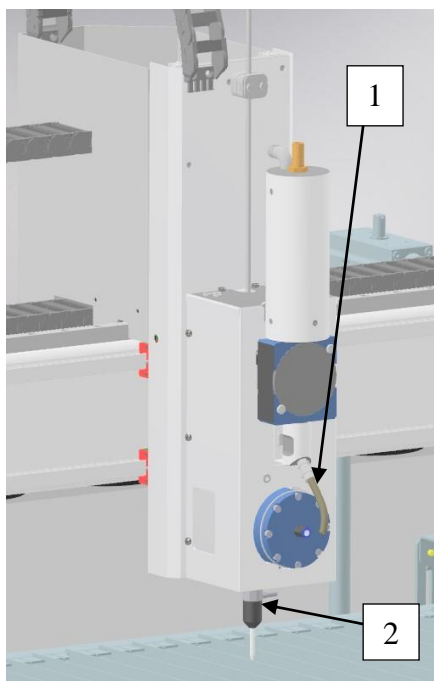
Werkzeughalter mit Abrasiv Dosierung
